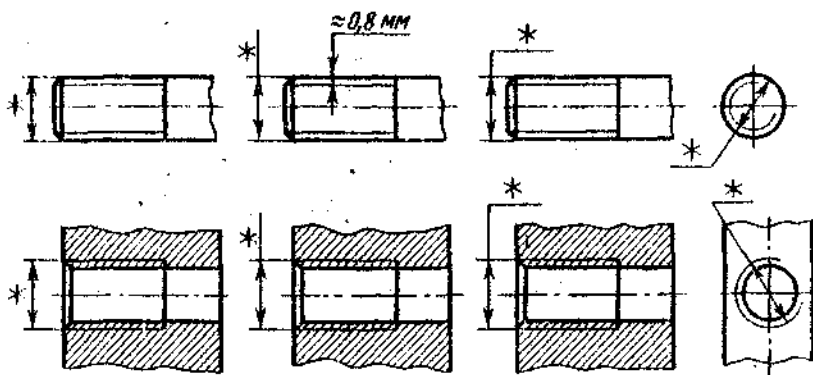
Допускаемые места нанесения обозначения резьбы
